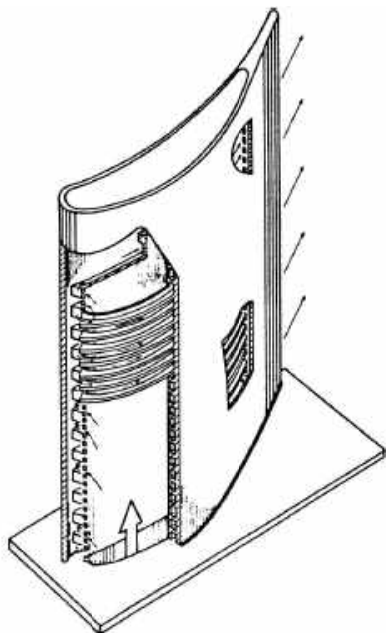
Схема дефлекторної робочої лопатки
